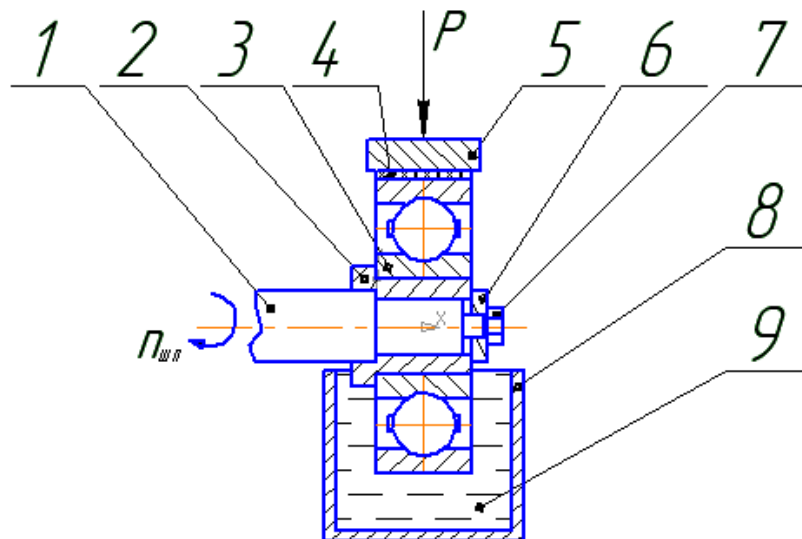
Схема обработки подшипников на машине трения МИ-1М:
